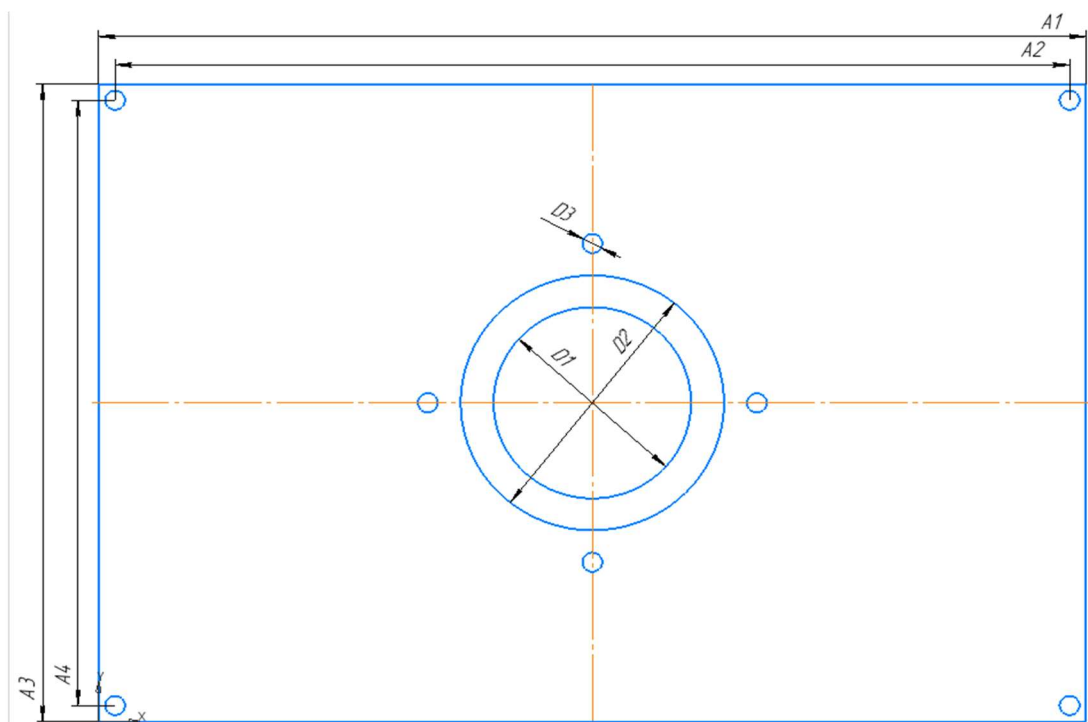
Чертеж детали робота-манипулятора (вид сверху)
